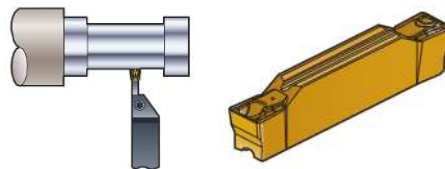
Інструмент для обробки зовнішніх канавок
